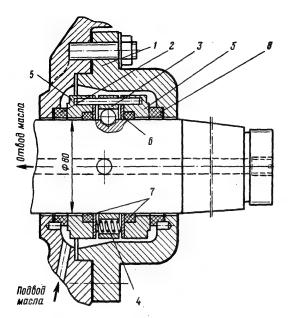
Сальник пружинный уплотнения конца вала (компрессор П80):
